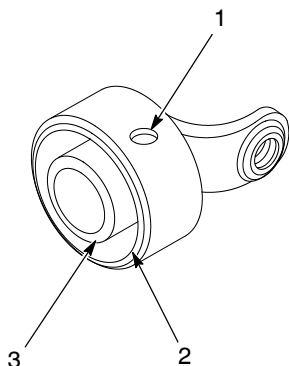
Instalace montážních skupin k upevnění pistole pomocí trubky
